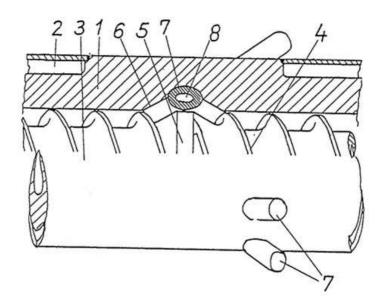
Шнековой экструдер по патенту РФ 2108911[11]: 1 – корпус; 2 – камера для нагрева; 3 – шнек; 4 – виток шнека; 5 – цилиндрическая часть шнека; 6 – выемка корпуса; 7 – штифт; 8 – отверстие
